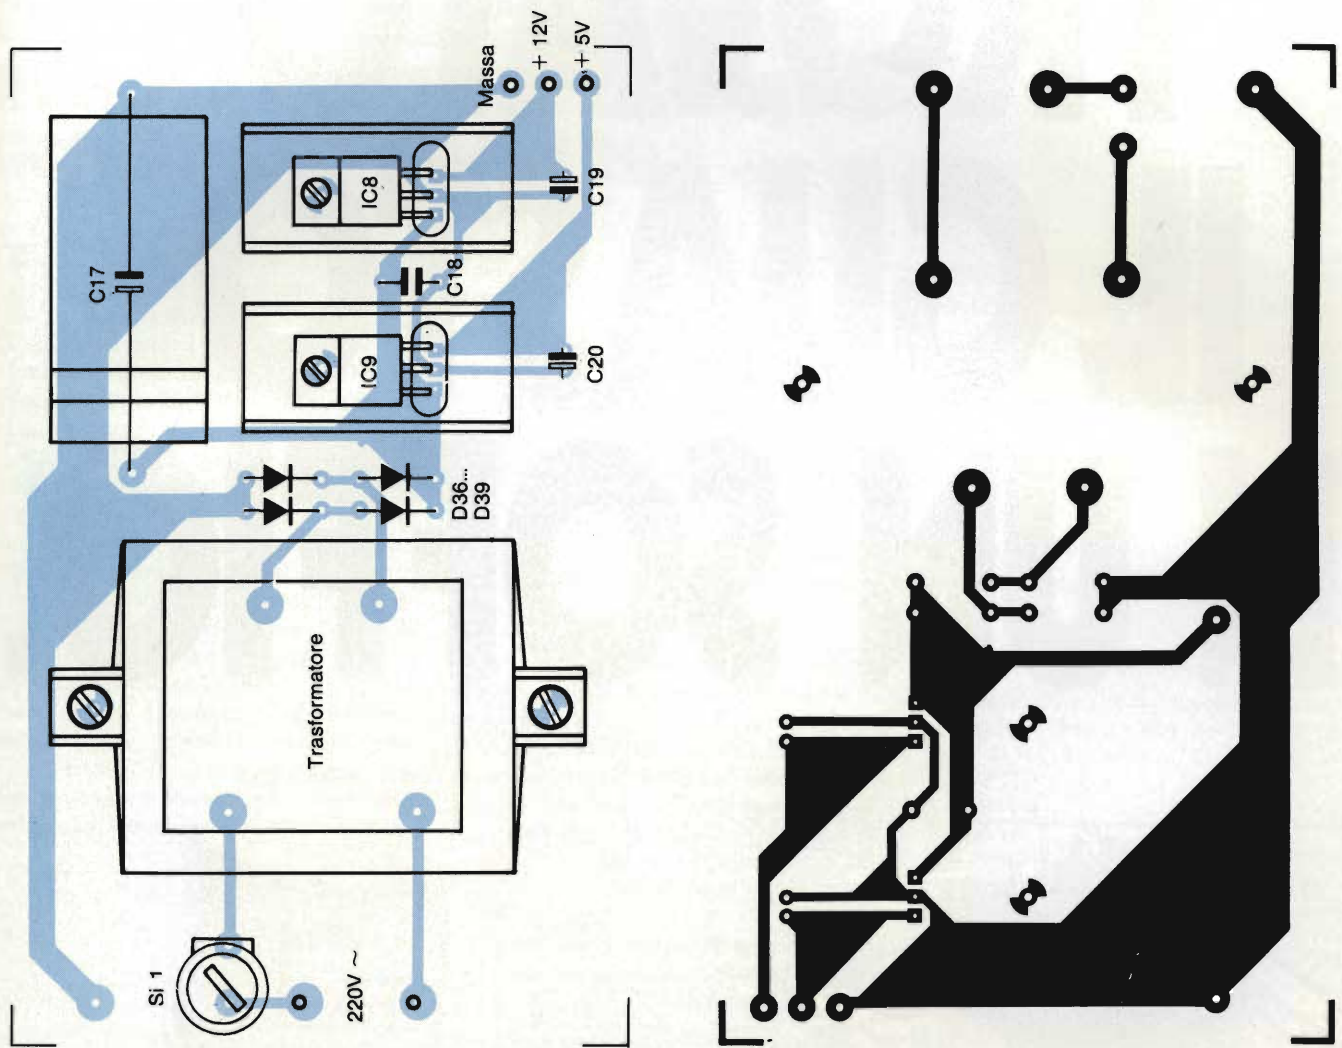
Pisté di rame e disposizione dei componenti sul circuito stampato della sezione alimentatore.
